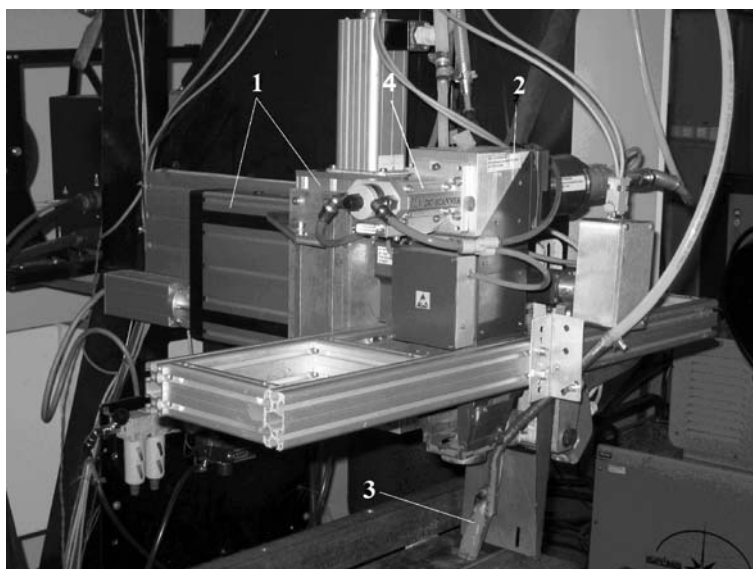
Рабочий инструмент лазерно-дугового модуля:
